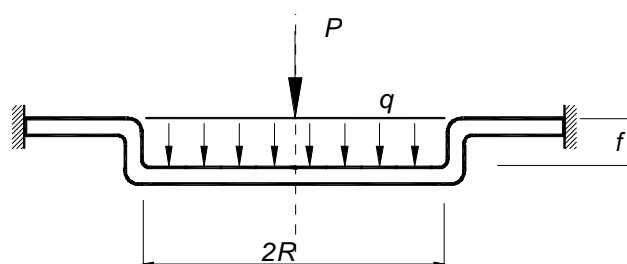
Схема деформирования листовой заготовки цилиндрическим пуансоном
